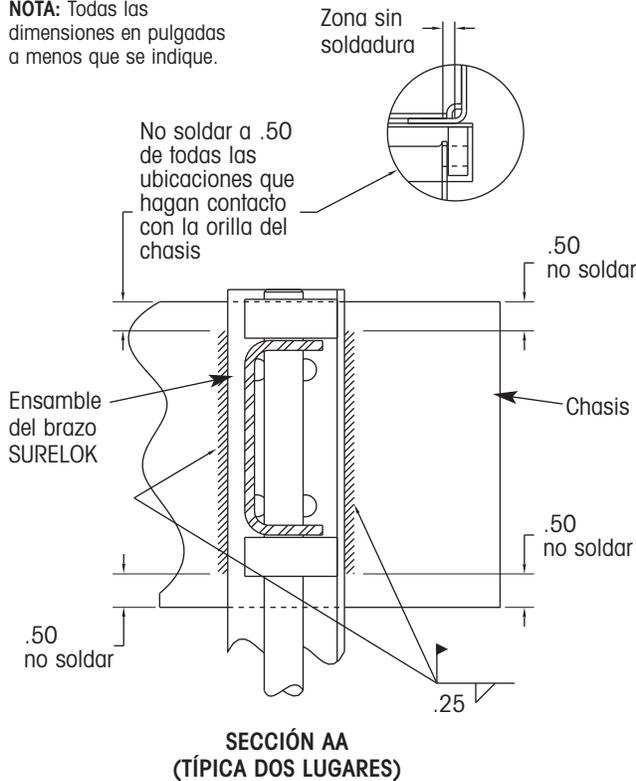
Detalles de soldadura del Kit SLKF
